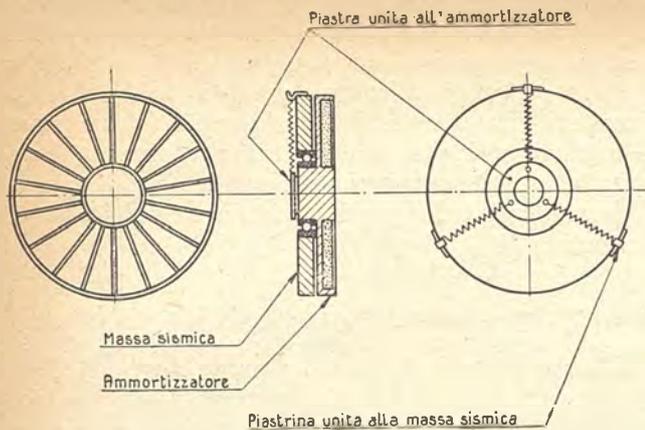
Ammortizzatore ad inerzia di liquido. Schema di dispositivo di prova.
